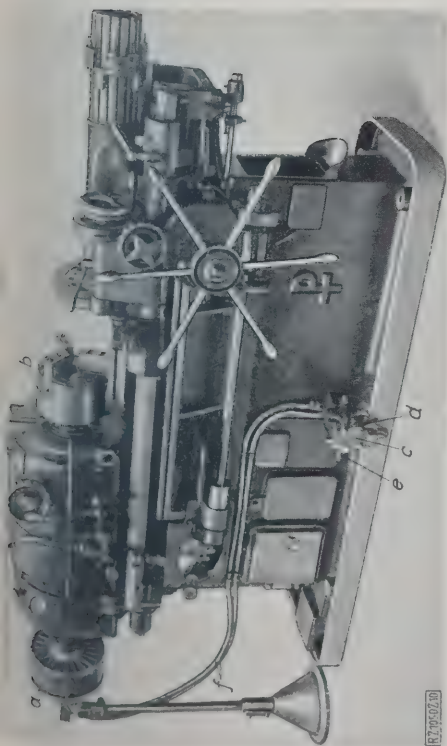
Revolverdrehbank der Werkzeugmaschinenfabrik Pittler, A.-G., Leipzig-Wahren, mit wagerechtem Revolverkopf für 16 Werkzeuge.
